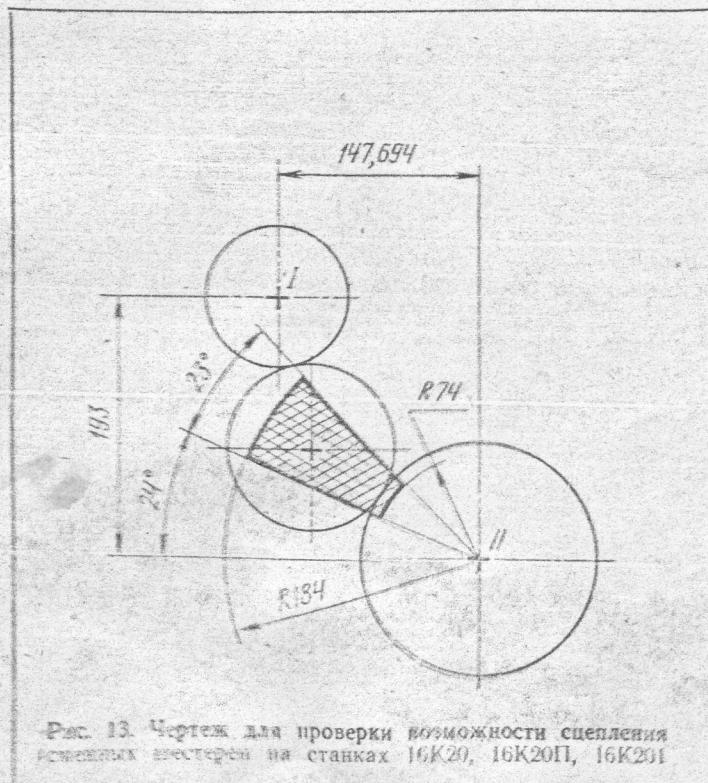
Чертеж для проверки возможности сцепления сменных шестерен на станках 16К20, 16К20П, 16К20Г
